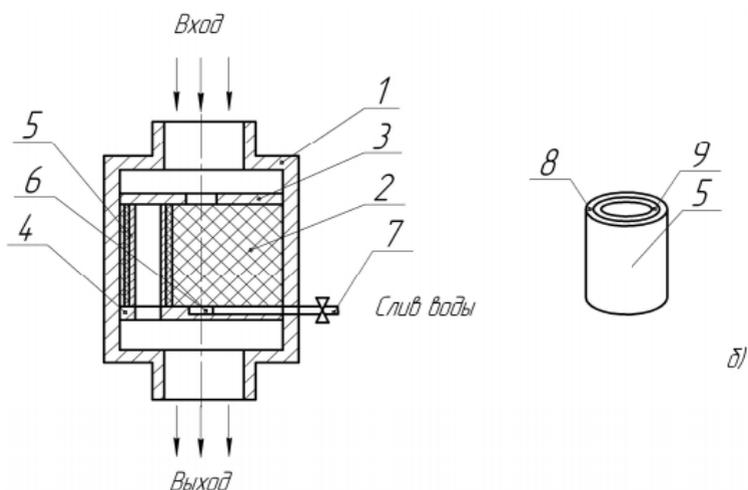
Фильтр сепаратор: 1 – корпус; 2 – пакет фильтрующего материала; 3, 4 – распределительные решетки; 5 – двухслойные трубчатые фильтроэлементы; 6 – коаксиальные каналы; 7 – сливное отверстие; 8 – слой из спеченного порошкового материала; 9 – слой из гидрофобного материала
